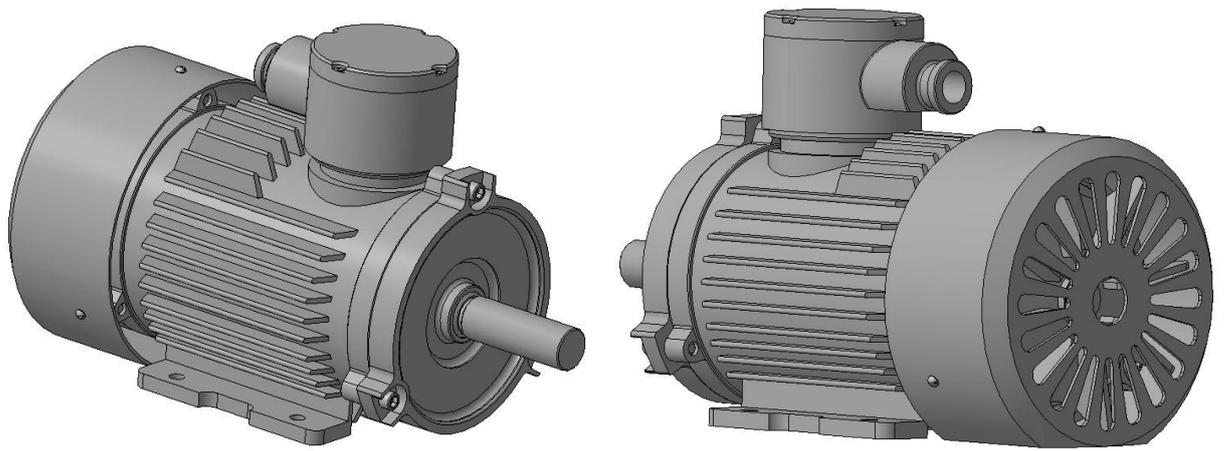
Сборочная 3D-модель узла пресса «Электродвигатель»
